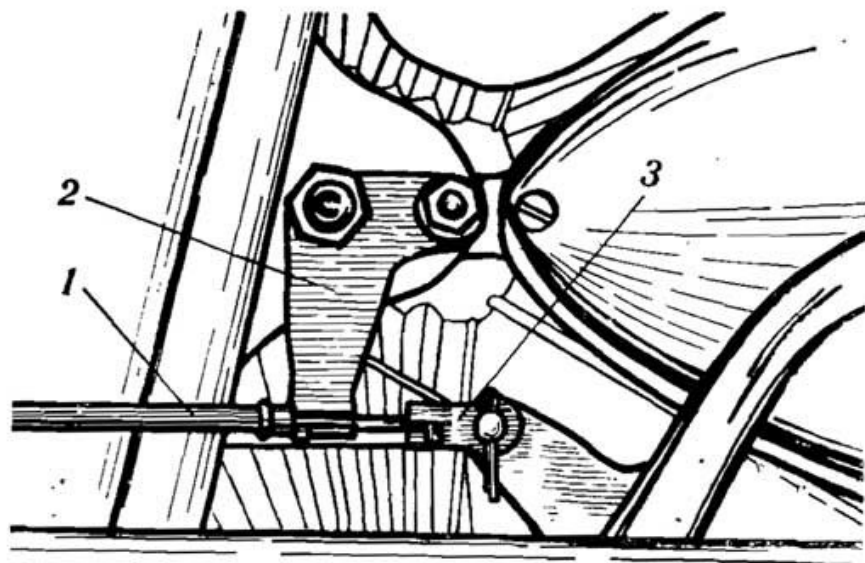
MONTAGE DU CÂBLE DE FREIN:
